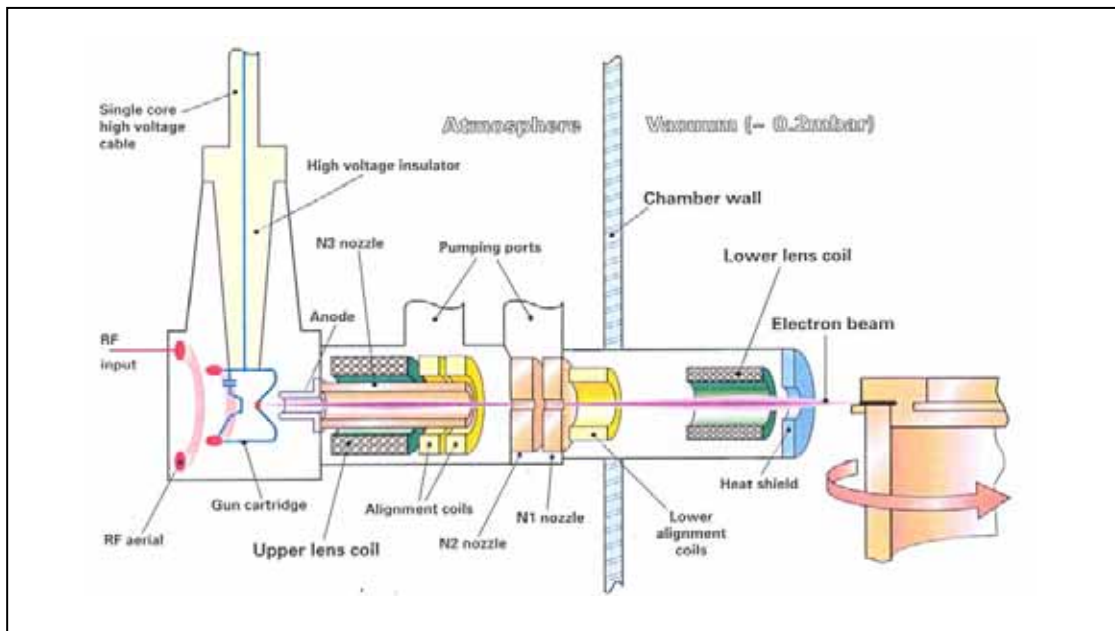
Enceinte de soudage sous vide
